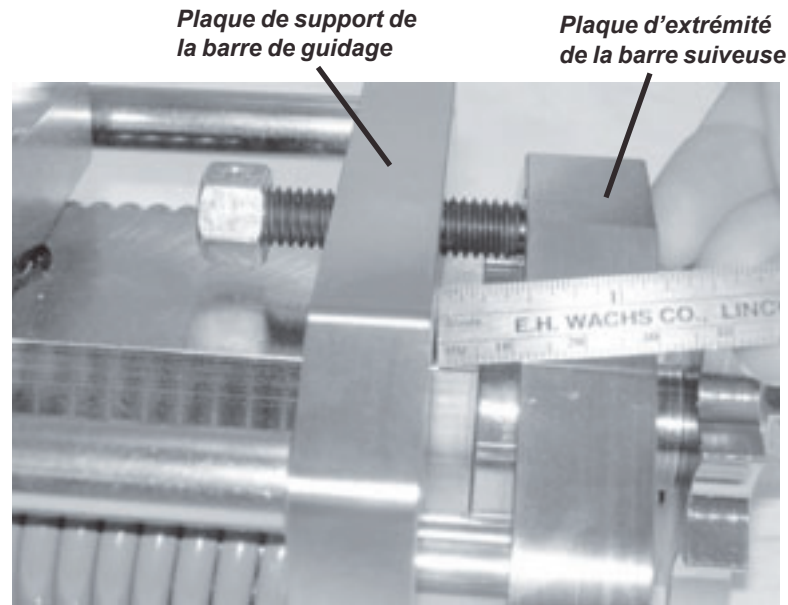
Vérifiez qu'il y a un jeu d'au moins 1/2" entre la plaque de support et la plaque à l'extrémité.
